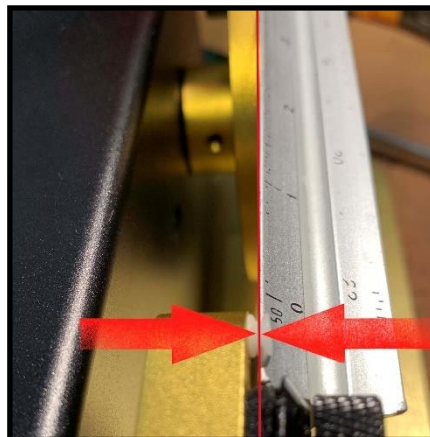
Einstellen des Versatzes zum Ausrichten der Drehplatte mit der Drahtführung
